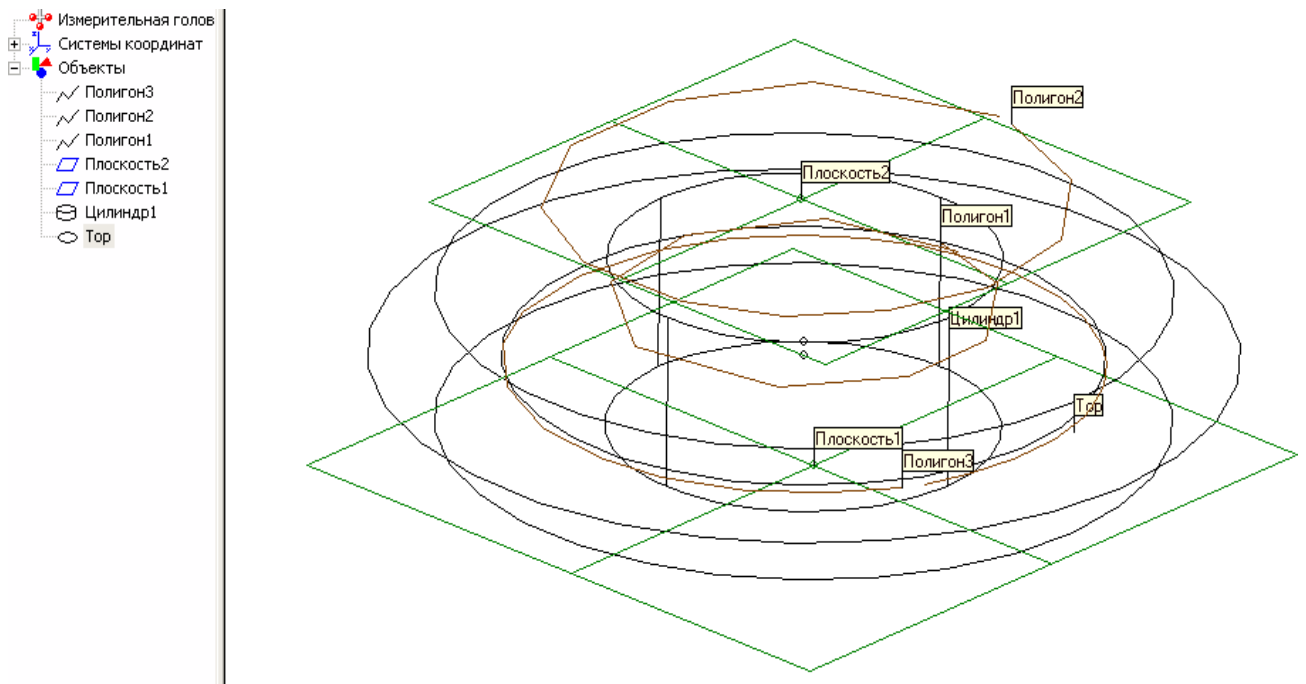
Сеанс вимірювання кільця кулькового підшипника
